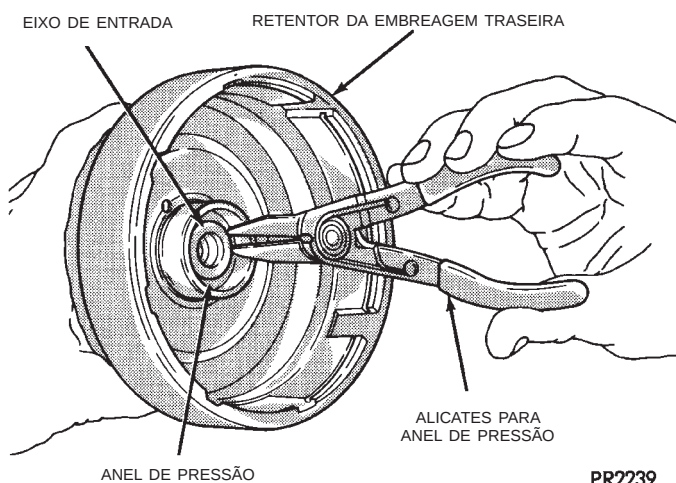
Remoção ou Instalação do Anel de Pressão do Eixo de Entrada
